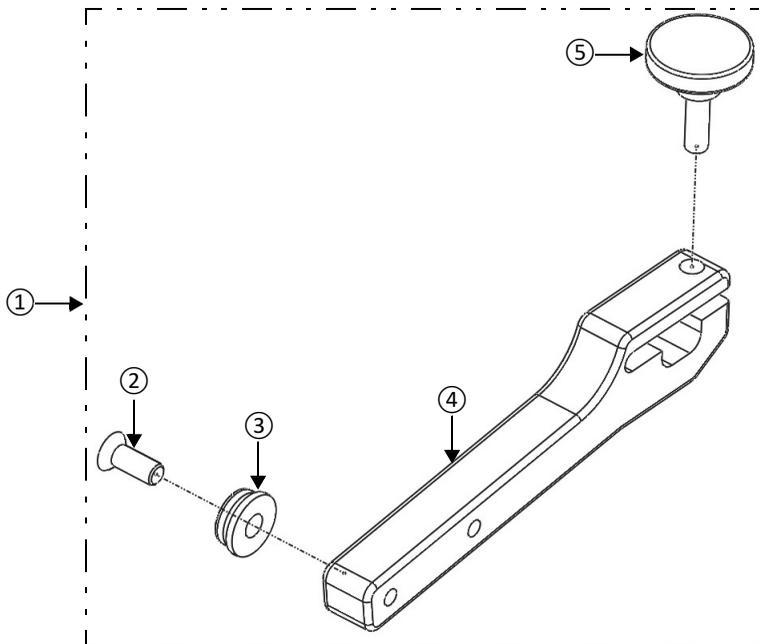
Рычаг вилки ФР в разобранном виде
